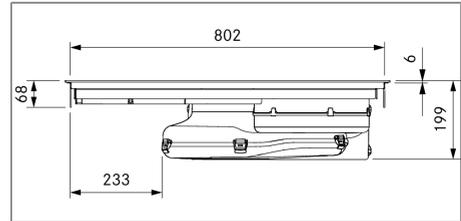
Dimensioni apparecchio PUXU vista frontale
